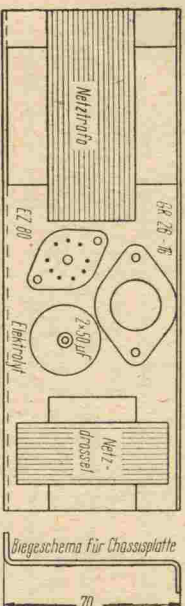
Aufbauschema für das Chassis des Universal-Netzgerätes. (Die Stabilisatorröhre ist richtig „SIR 150/40 z“)
